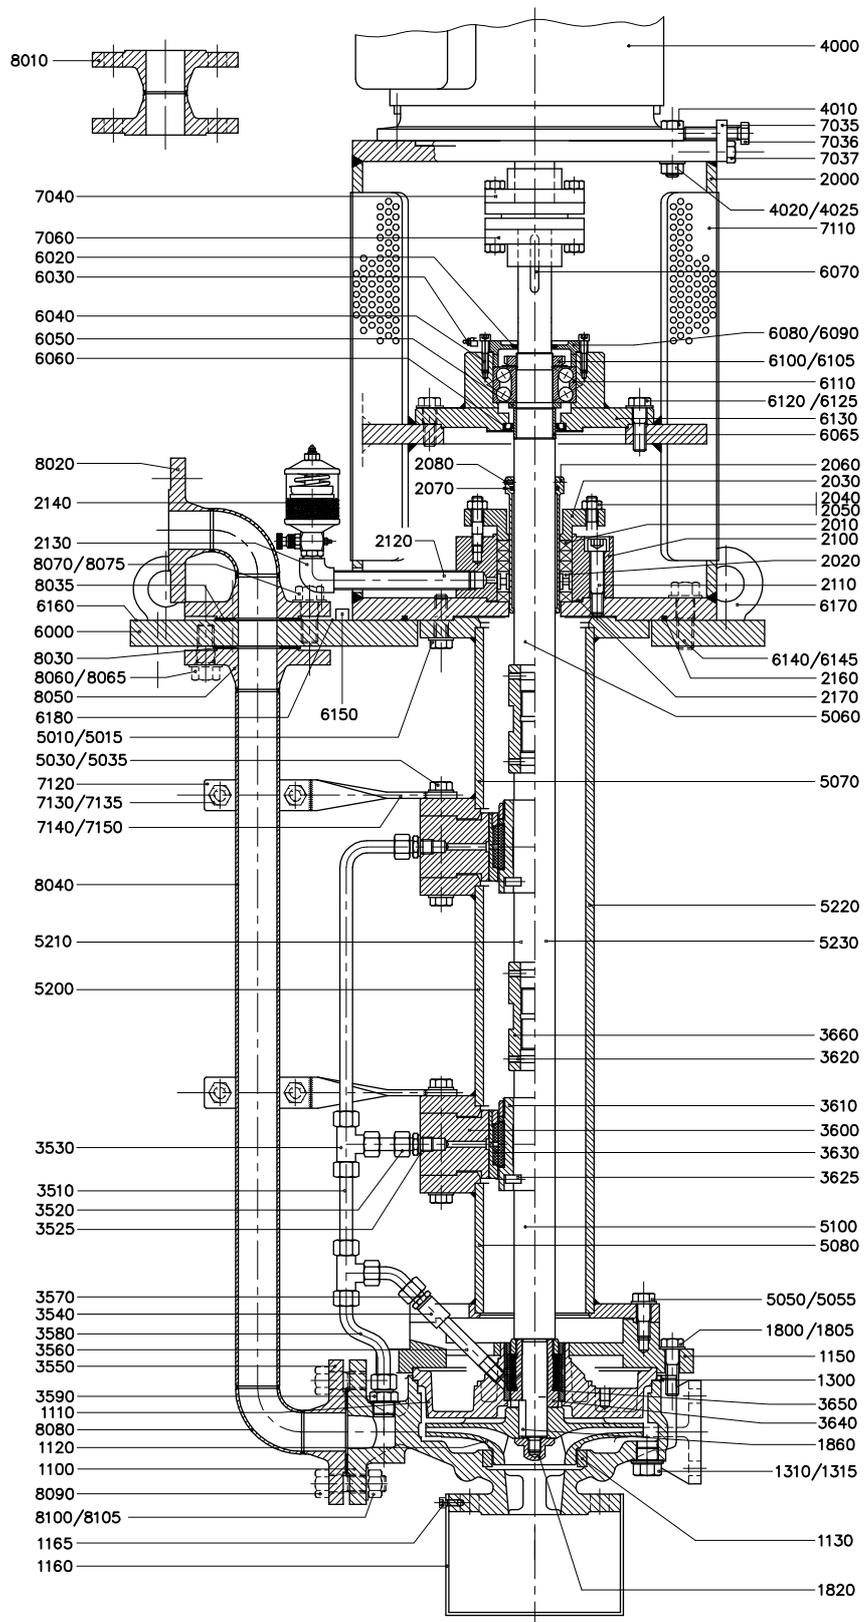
Pompe avec groupe d'étanchéité d'arbre S3.
